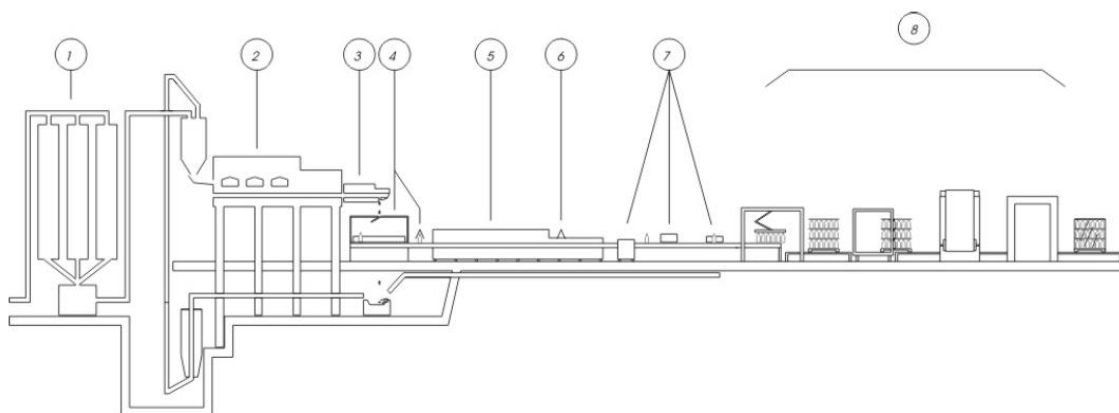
Fluxograma do processo do fabrico do vidro de embalagem. 1 - Composição; 2 - Fusão; 3 - Condicionamento térmico; 4 - Moldagem e TSQ; 5 - Recozimento; 6 - TSF; 7 - Inspeção; 8 - Embalagem.
